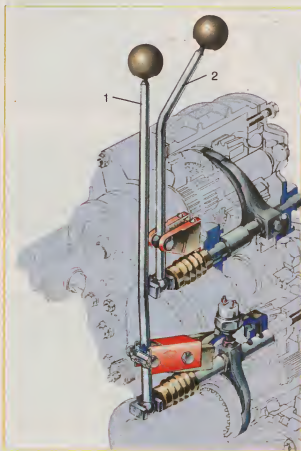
Расположение рычагов раздаточной коробки: 1 – рычаг блокировки; 2 – рычаг переключения.
